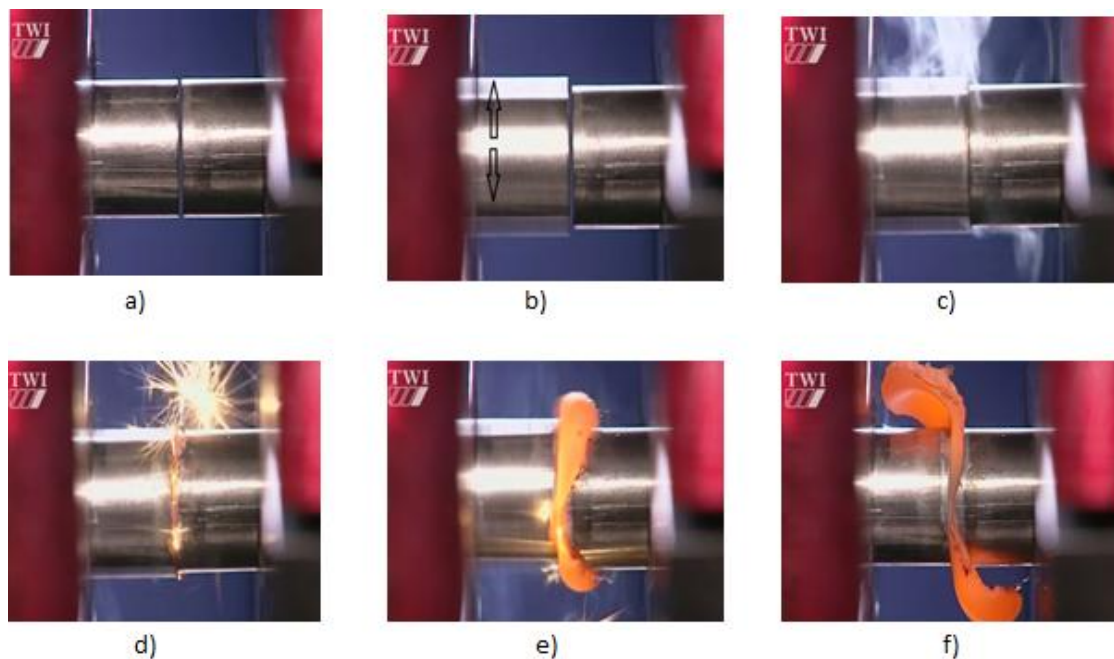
Processo de soldadura por fricção linear (SFL): a) posicionamento inicial; b) movimentação da peça; c) aumento da temperatura local; d), e), f) ocorrência da soldadura
